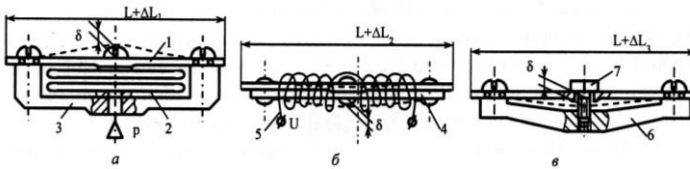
Конструктивна реалізація варіантів приводів для деформації плоских пружин: а – сифонний привод; б – термомеханічний привод; в – механічний гвинтовий привод
